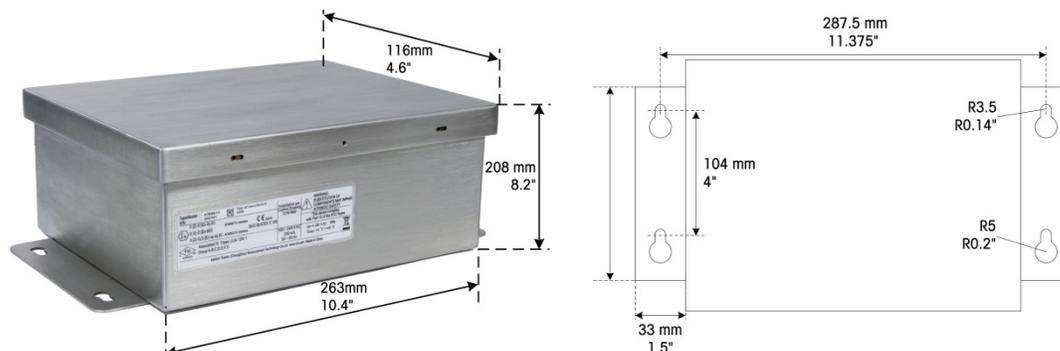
Dimensões do Módulo de Comunicação ACM500
